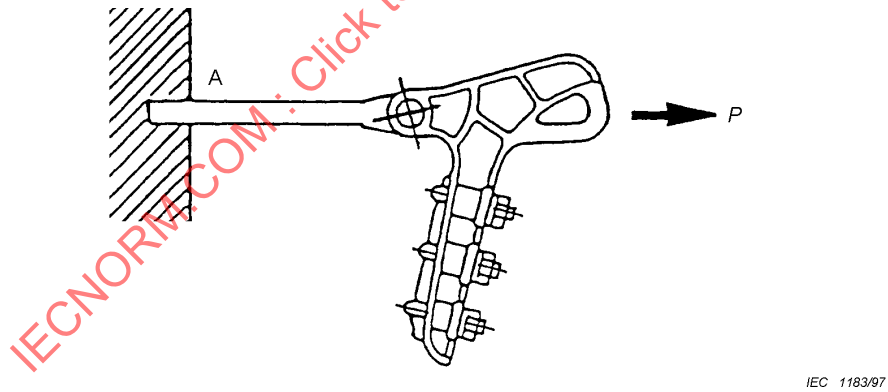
Pinces d'ancrage et manchons d'ancrage – essai de charge d'endommagement et de rupture du point de fixation utilisé au montage: croquis montrant l'application type de la charge
